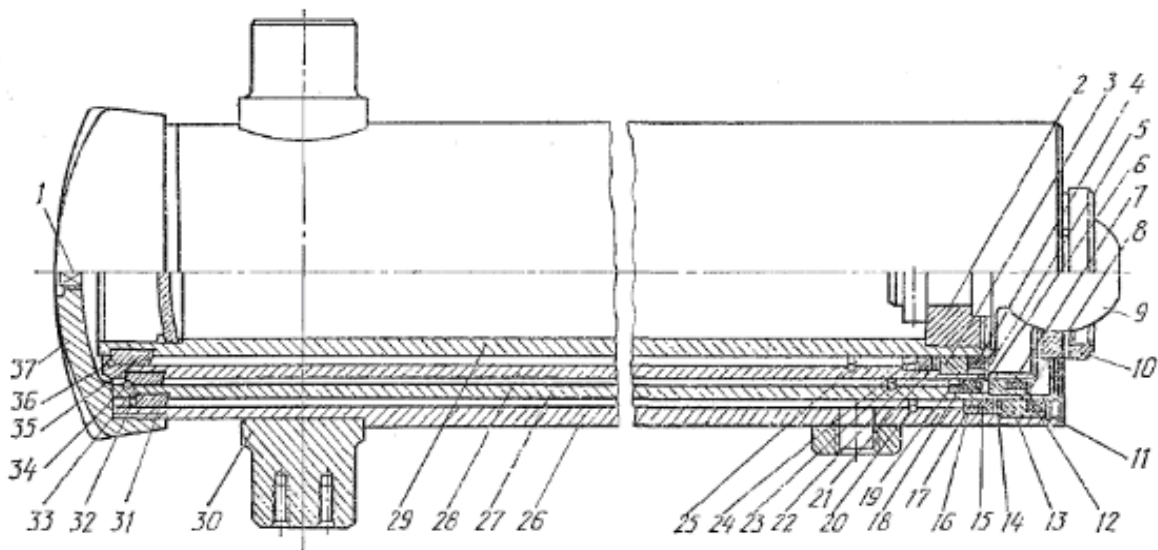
Гидроцилиндр опрокидывающего механизма платформы самосвала МАЗ-5549
